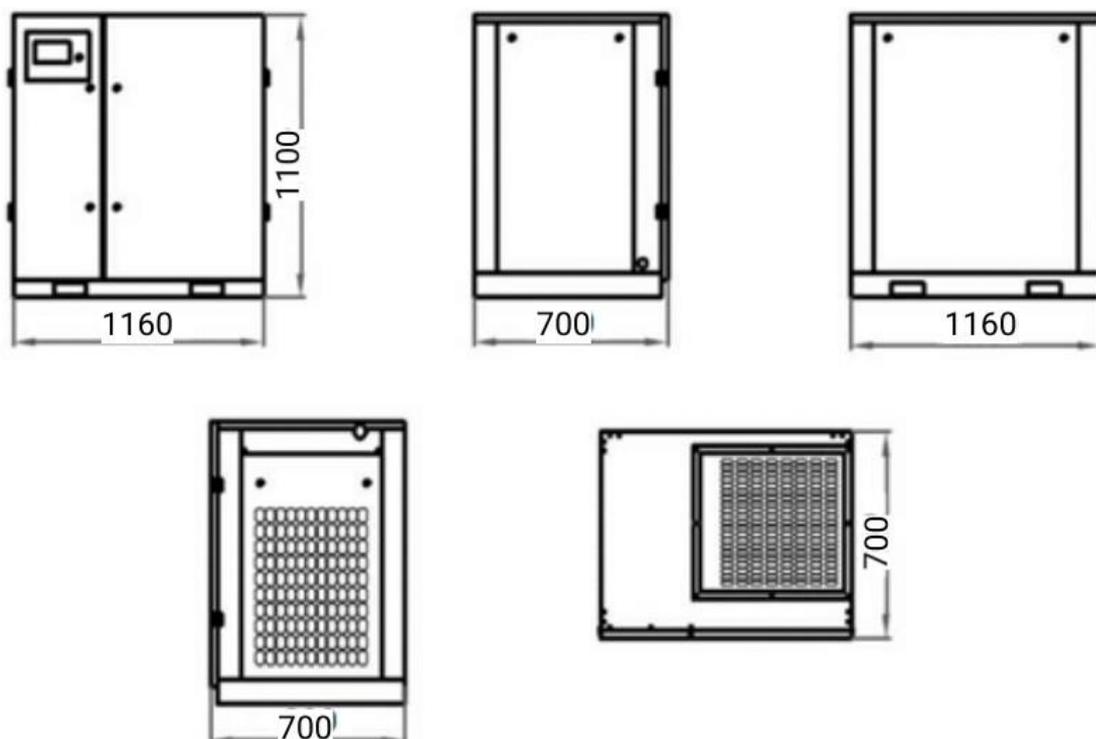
Габаритные размеры компрессоров BRM-15A
